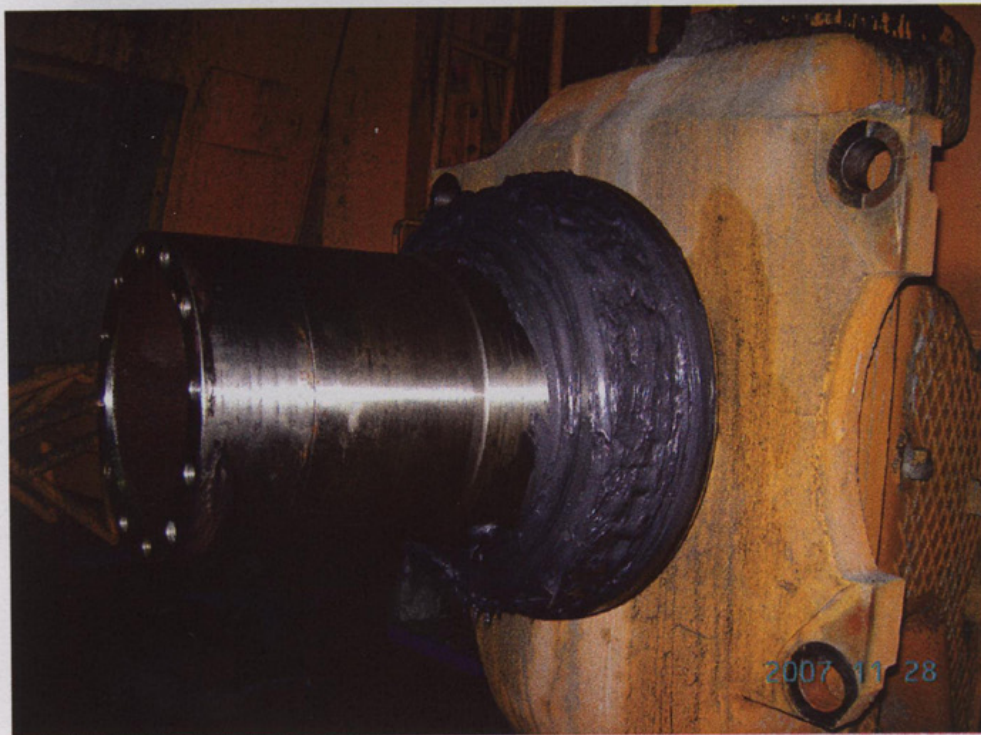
Смазка МС-1000 нанесённая на подшипник перед сборкой ступицы.
